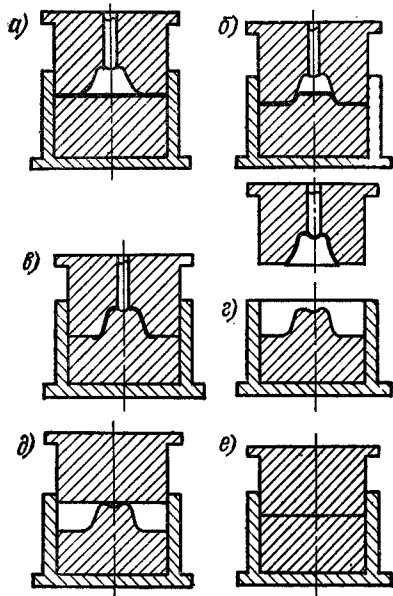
Способ штамповки-вытяжки свинцом по металлической матрице
